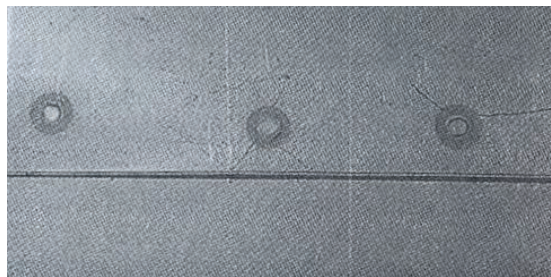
Зварний шов, утворений контактнo-точковим зварюванням
